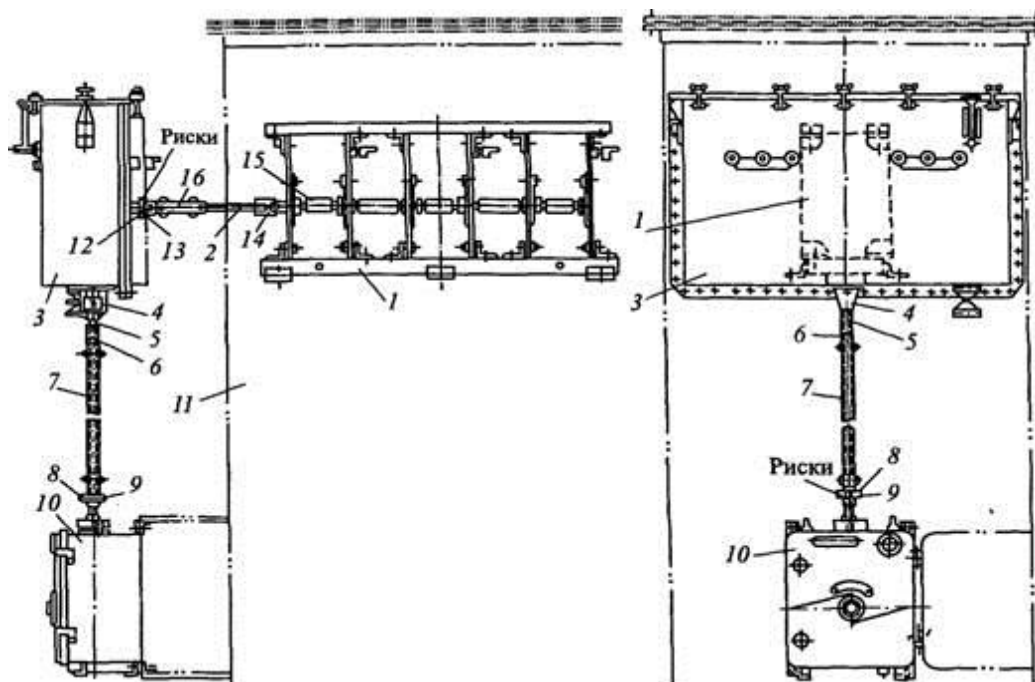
Аппараты переключающего устройства типа РНТ, установленные на трансформаторе: 1 — переключатель; 2 — горизонтальный пал; 3 — бак контакторов; 4 — сальник; 5 — вал сальника; 6 — переходная муфта вертикального вала; 7 — вертикальный вал; 8 — нониусный диск вала (7); 9 — нониусный диск вала механизма (10); 10 — приводной механизм; 11 — бак трансформатора; 12, 13 — нониусные диски вала контакторов и карданного вала; 14 — соединительная муфта вала переключателя; 15 — вал переключателя; 16 — горизонтальный карданный вал.
